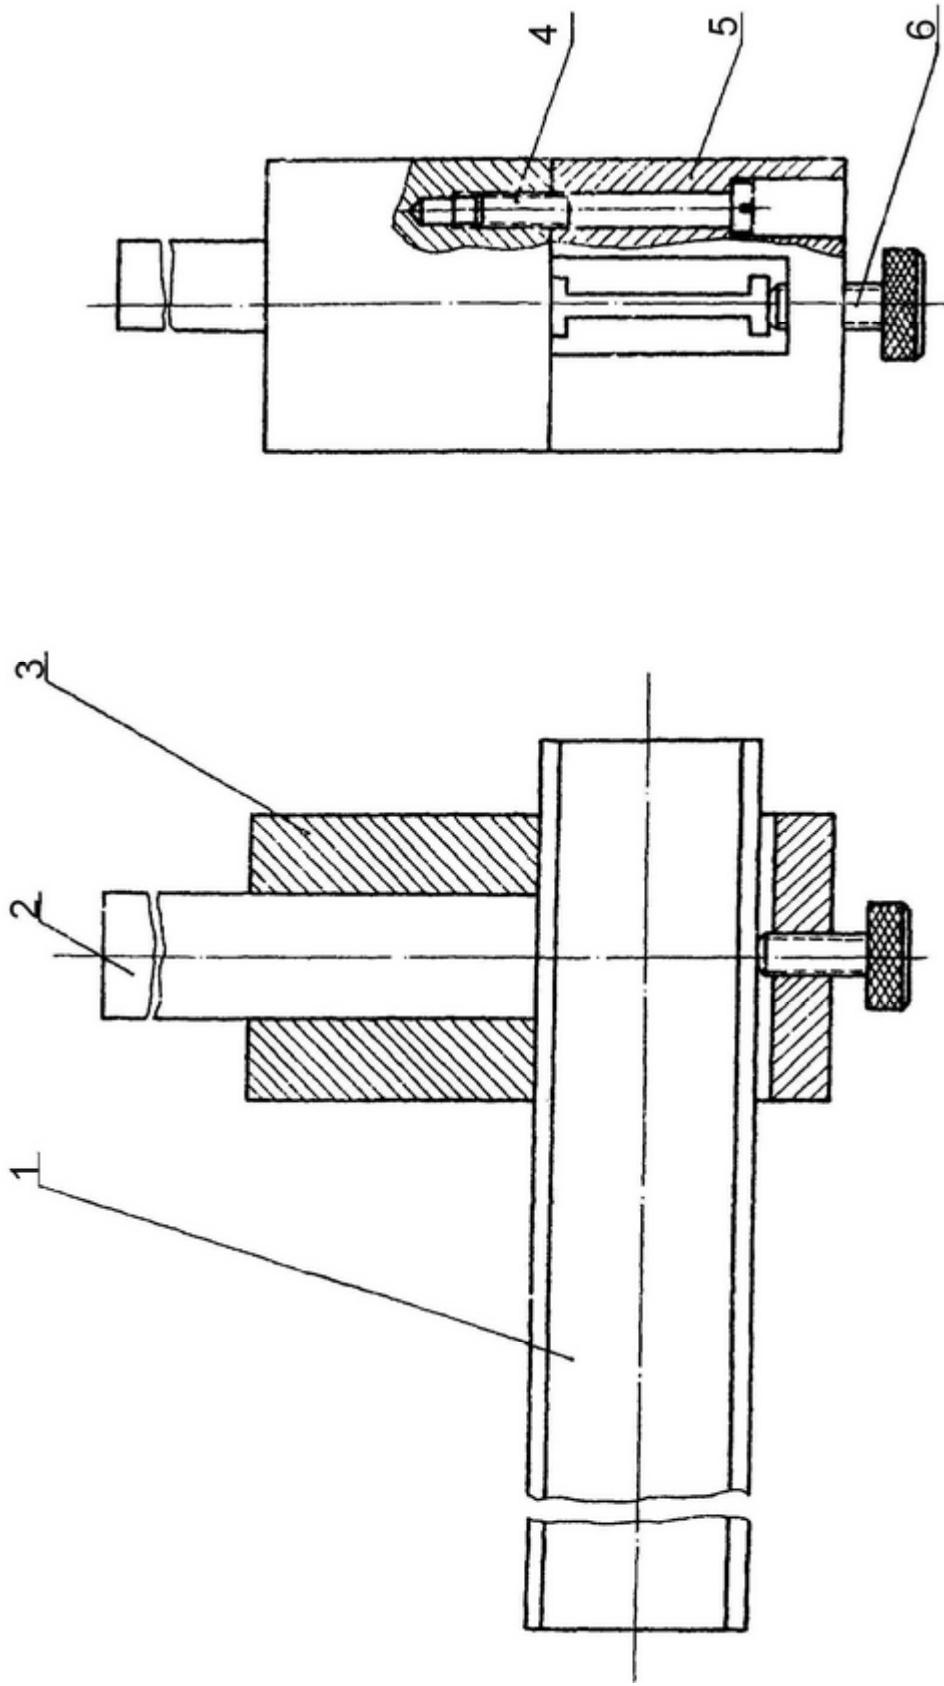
Приспособление для проверки перпендикулярности верхних направляющих каретки к направляющим станины СД 8532 – 4001
